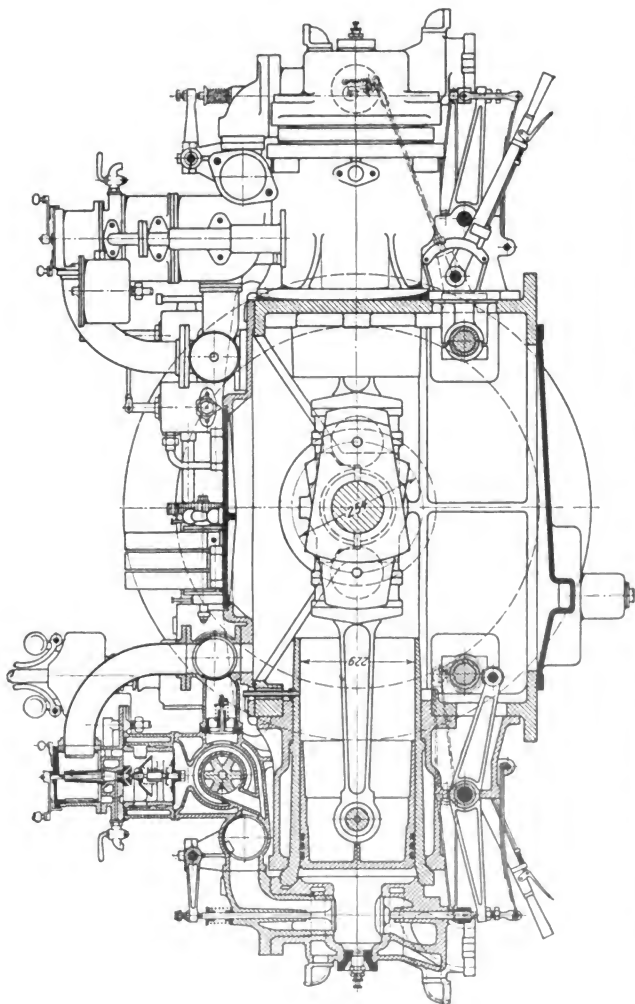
Schnitt durch den in Fig. 65/66 abgebildeten 140 PS-Wolsley Motor, in vergrößertem Maßstabe.
